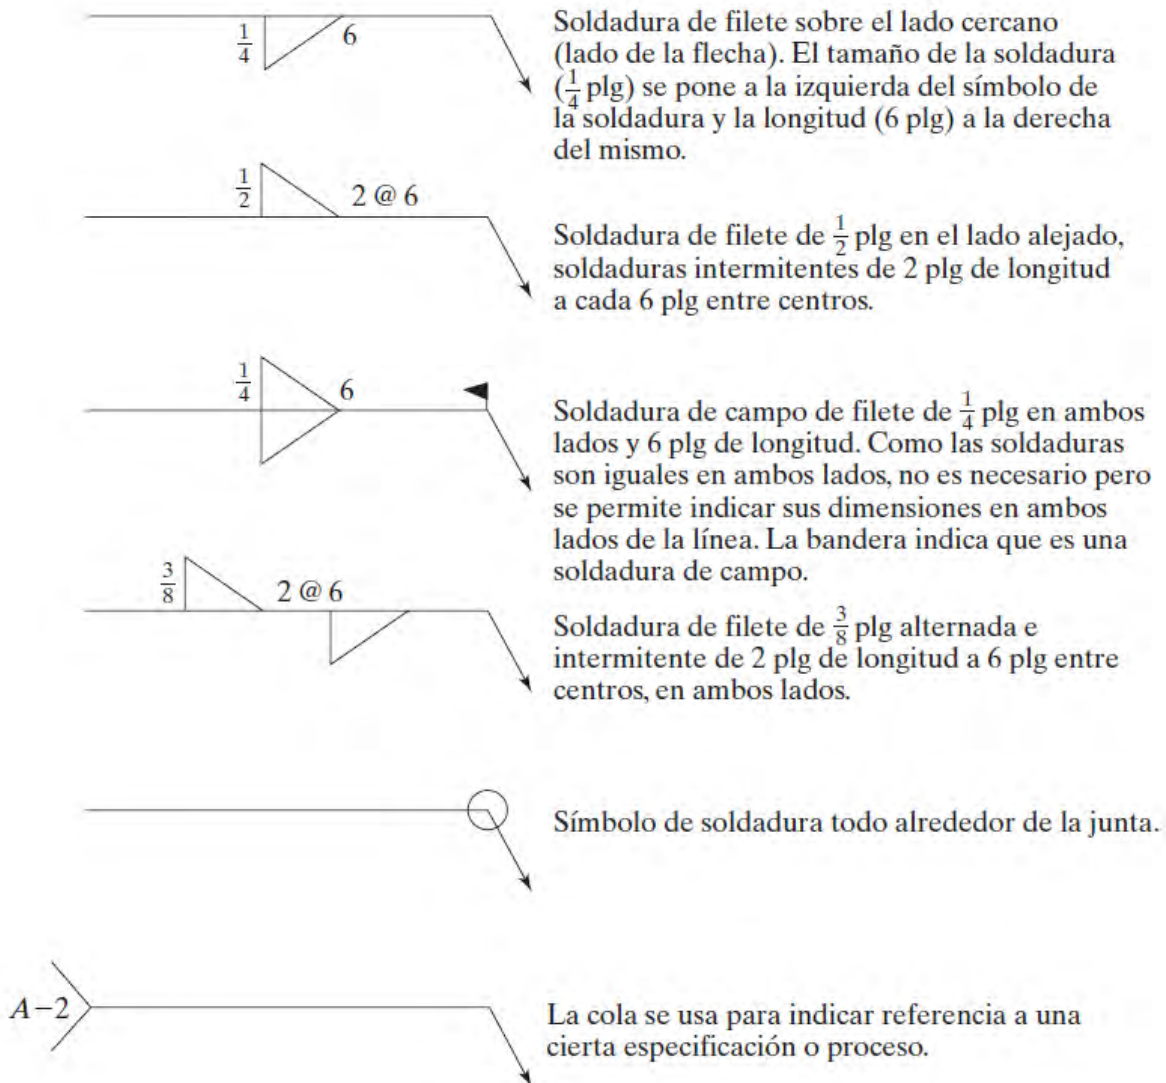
Ejemplos de símbolos de soldadura.
